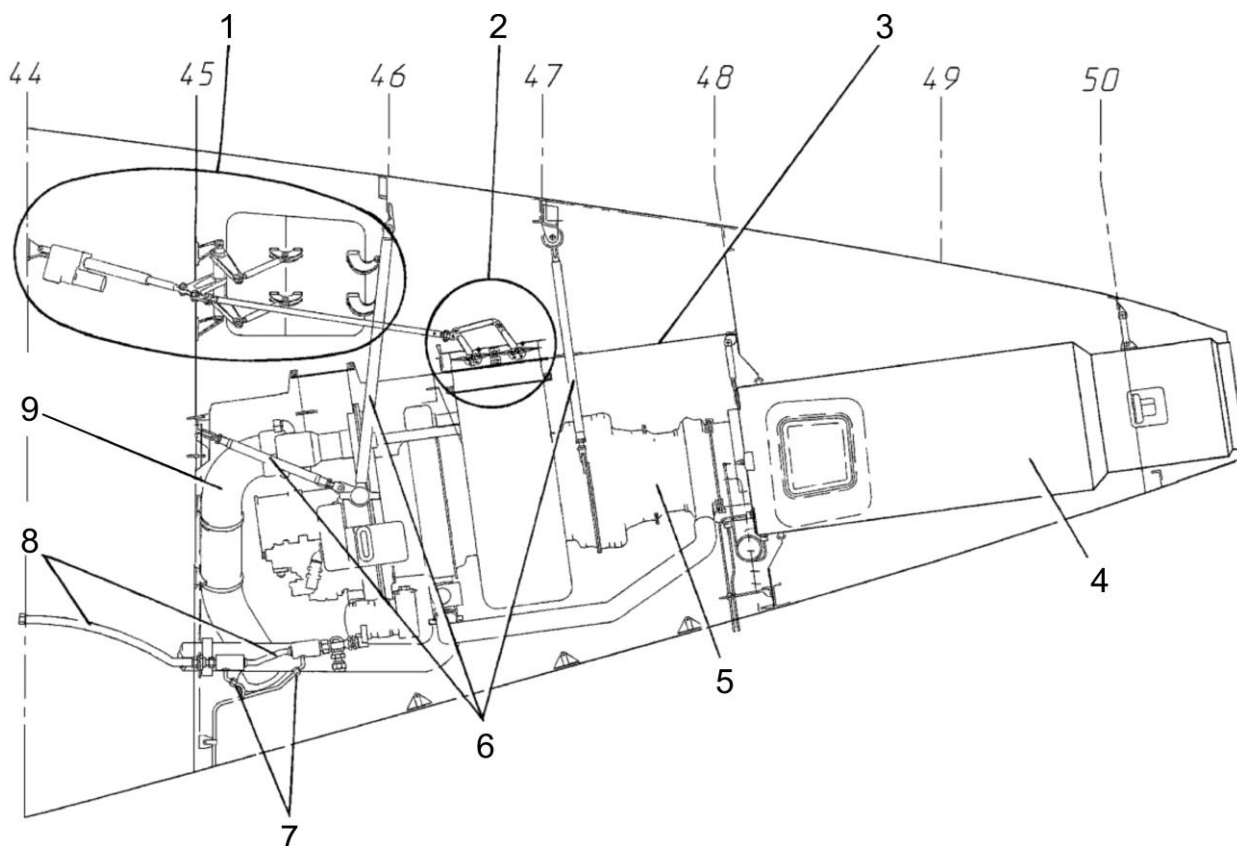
Схема крепления вспомогательной силовой установки:
